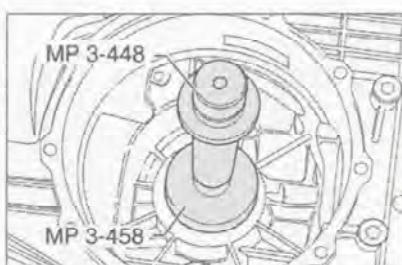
Установка наружной обоймы роликоподшипника в картере.
